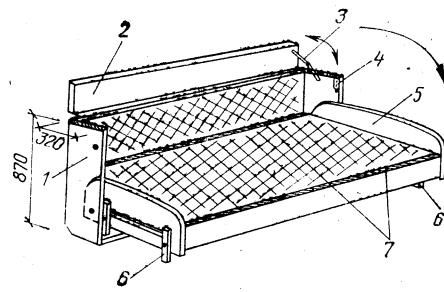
Трансформирующийся низ двухъярусной кровати в положении «кровать»: 1 — боковина; 2 — откидная доска; 3 — держатель-фиксатор; 4 — защелка-фиксатор; 5 — боковины (крылья) кровати-стола; 6 — опорные ножки; 7 — прижимные ленты
